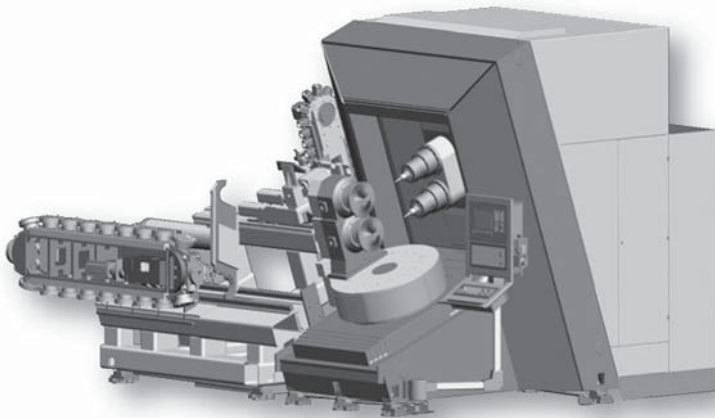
Centre d'usinage à 4 têtes d'outils.
